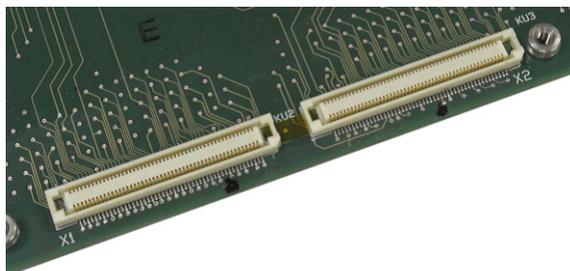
Gros plan des connecteurs ETX sur la carte principale
